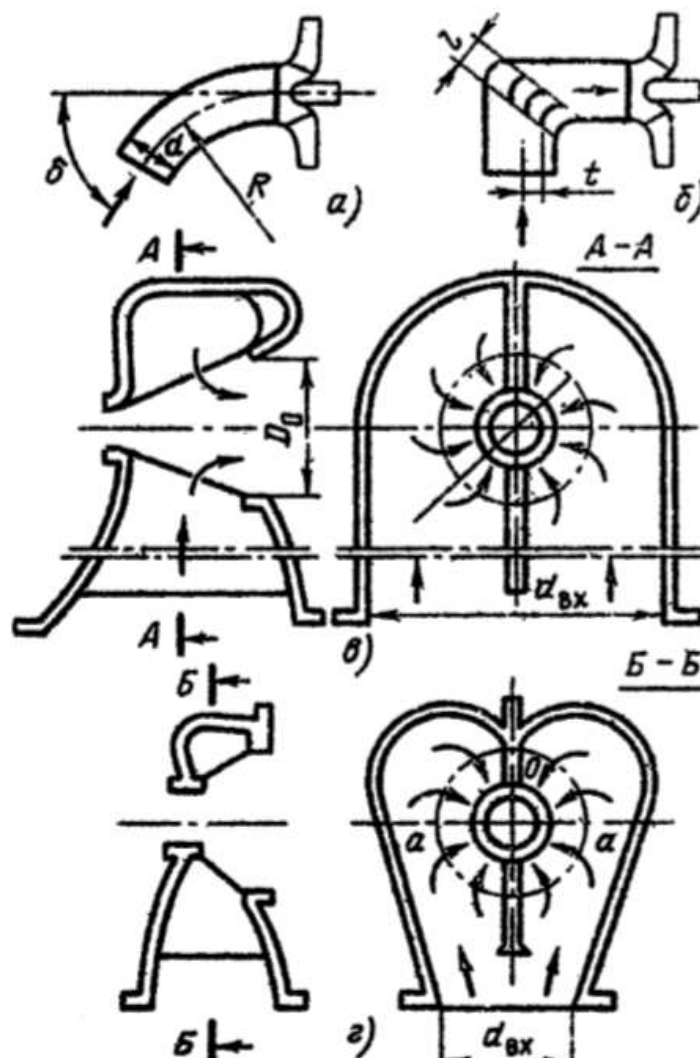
Боковые подводы компрессоров: а - угловое колено; б - колено с направляющими лопатками; в - кольцевой подвод; г - двухзаходный полуспиральный подвод
